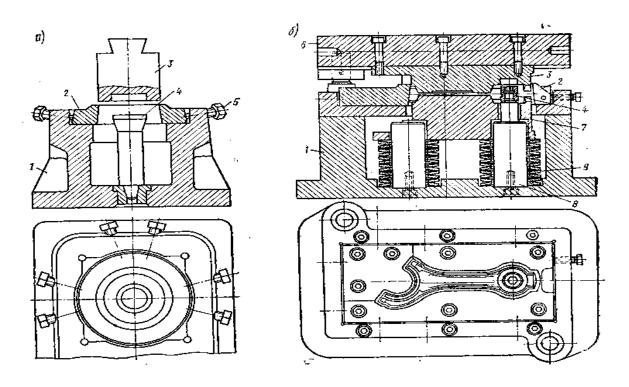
Схема обрезных штампов совмещенного действия: а — для обрезки облоя и прошивки отверстия (с ручным подъемом прошивня); б — для обрезки облоя и прошивки зева в поковке шатуна (с буферным устройством); 1 — нижний штамп; 2 — матрица; 3 — обрезной пуансон; 4 — прошивень; 5 — болт; 6 — верхний штамп; 7 — прижим; 8 — упор; 9 — пружина
